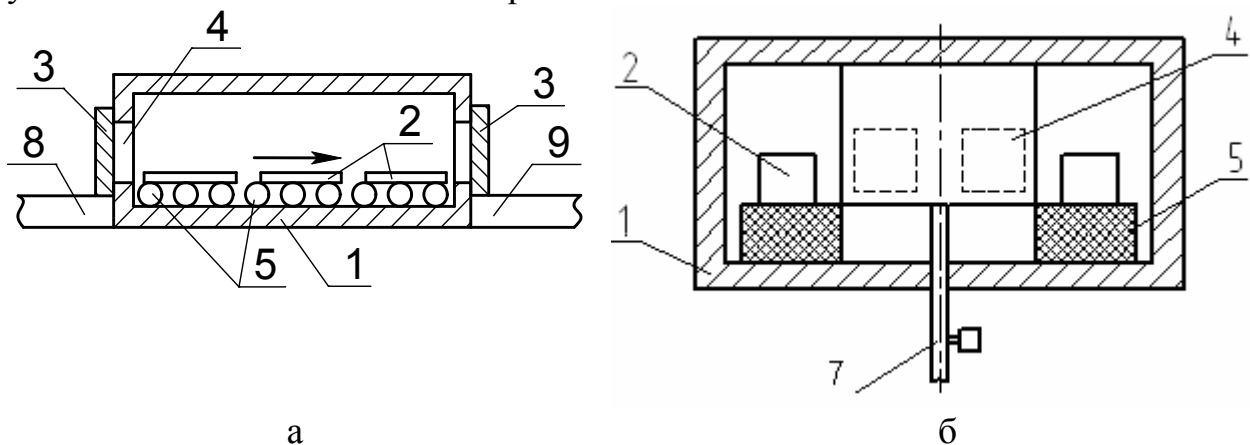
Схемы печей непрерывного действия: а – рольганговая; б – карусельная; 1 – каркас печи с футеровкой; 2 – нагреваемые тела (загрузка); 3 – дверца; 4 – загрузочные проемы; 5 – рольганг с приводом; 6 – кольцевой под; 7 – вал с приводом; 8 – загрузочный стол; 9 – разгрузочный стол
